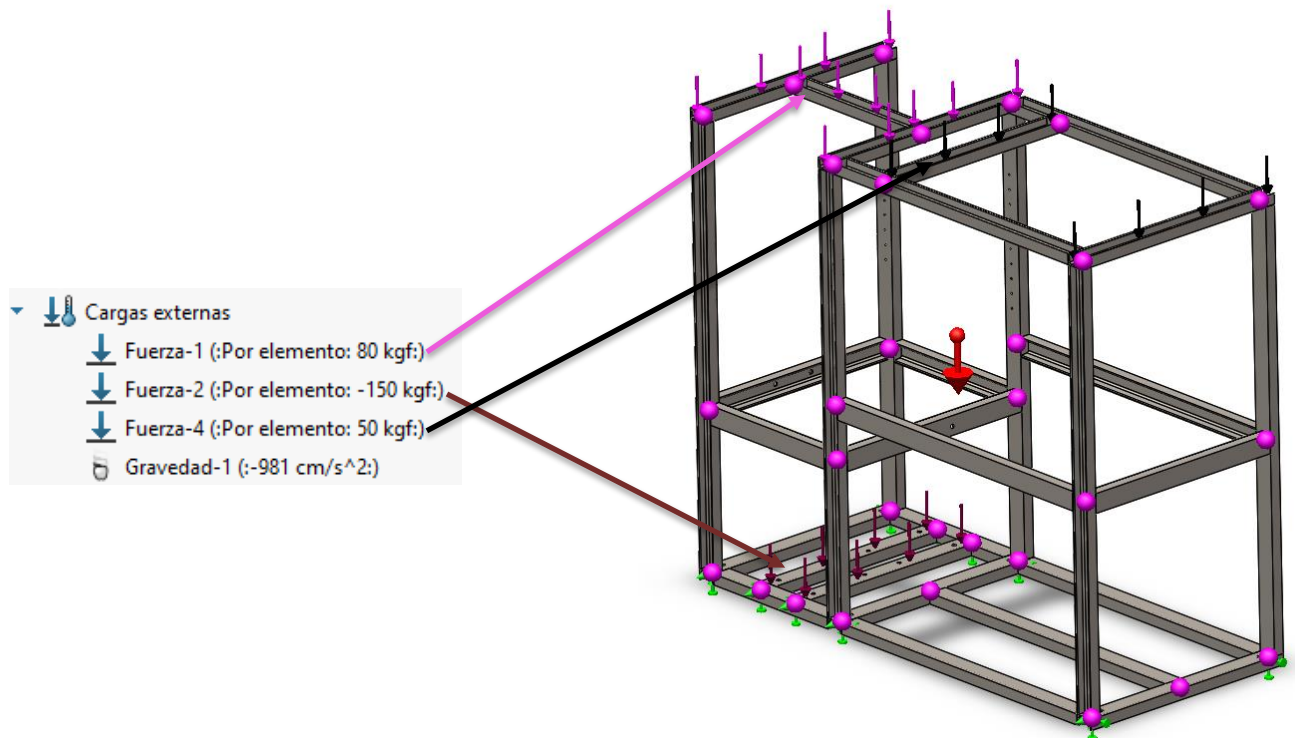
g: Cargas aplicadas en estructura.
